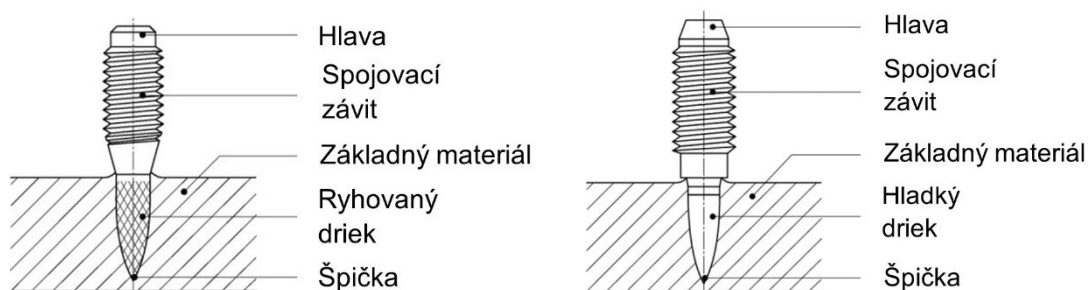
Komponenty spoja so závitovou skrutkou
